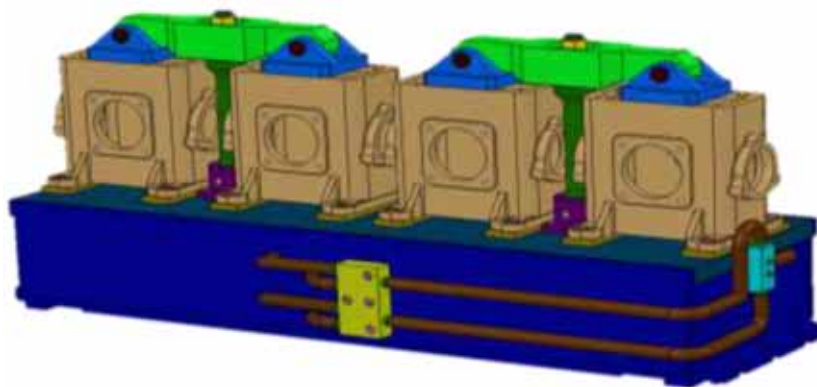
Пристосування для чистового фрезерування корпусів редукторів із встановленими редукторами.
